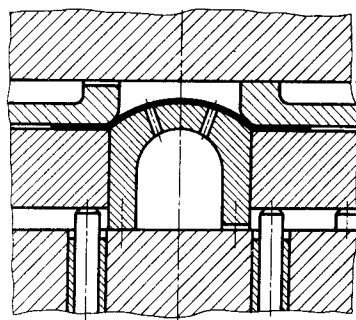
Пример конструкции вытяжного штампа для выпуклой детали, когда допускается выполнять матрицу с вертикальными стенками
